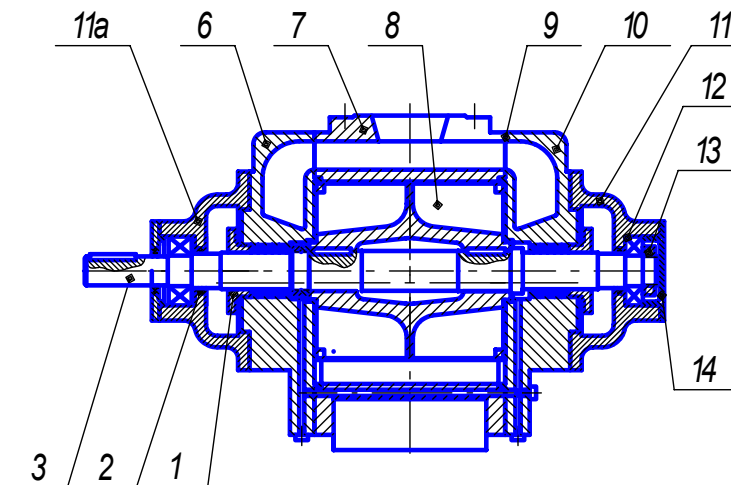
Разрез вакуум-насоса и компрессора типоразмерного ряда
